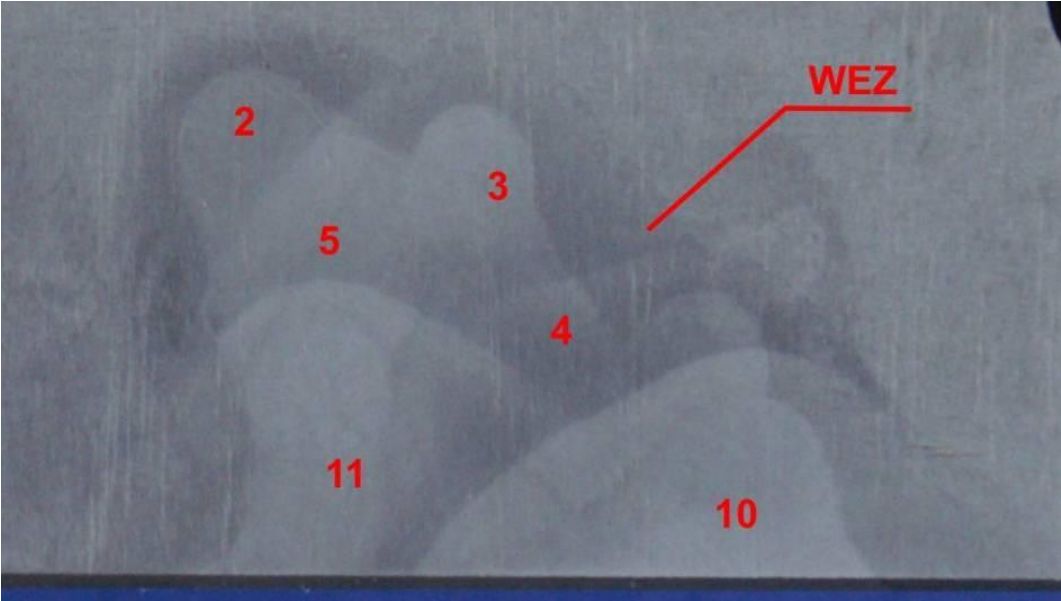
Probe 02 - Ansicht unterer Teil der Schweißnaht
